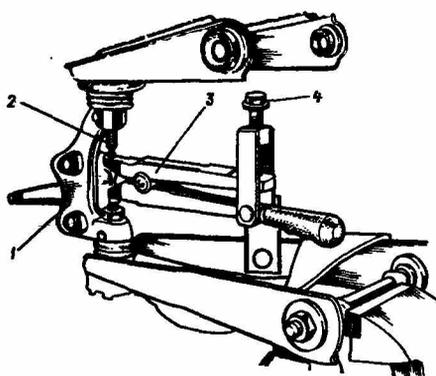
Отсоединение верхнего рычага: 1 - поворотный кулак; 2 - палец шарового шарнира; 3 - приспособление 67.7801.9513; 4 - болт
